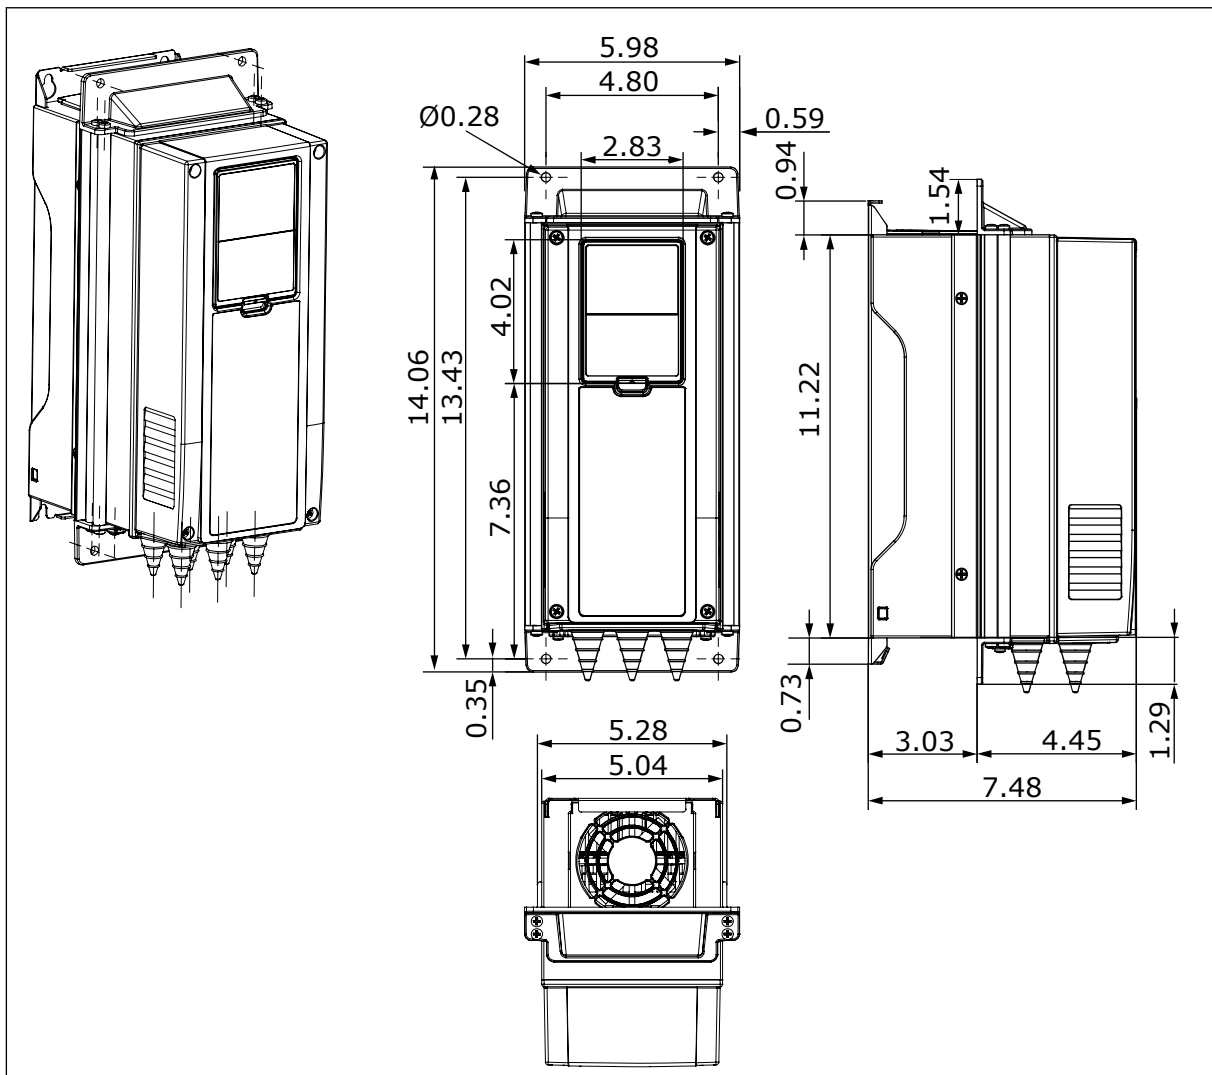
Dimensioni dell'inverter, montaggio a flangia, MR4 [pollici]
